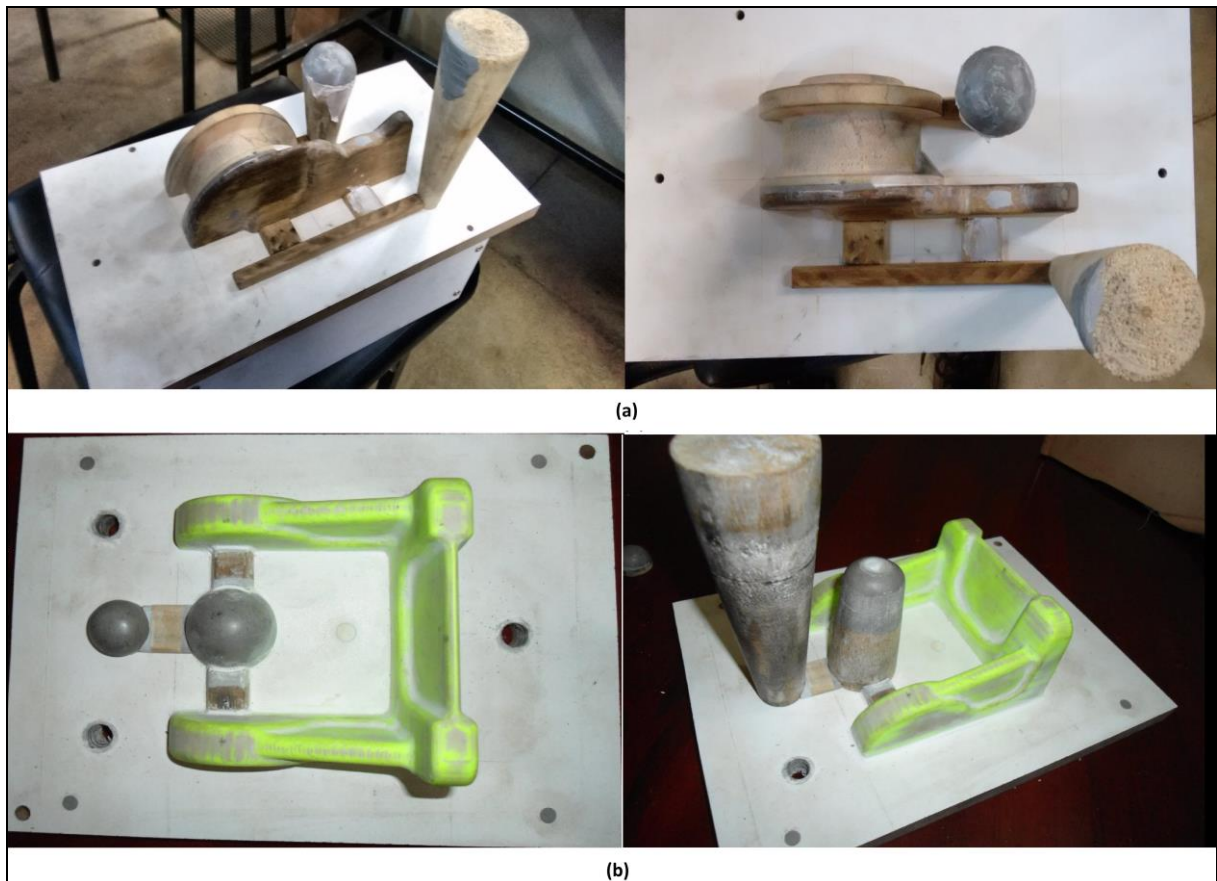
Placas para moldagem . (a) Placa de moldagem para a peça Base; (b) Placa de moldagem para a peça Mancal.
